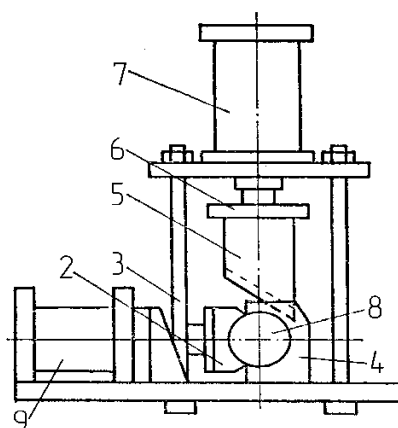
Станок для резки труб клиновидным ножом: 1 - стол; 2 - прижим; 3 - колонки; 4 - матрица; 5 - нож; 6 - траверса ножа; 7 - пневмоцилиндр реза; 8 - перерезаемая труба; 9 - пневмоцилиндр прижима
